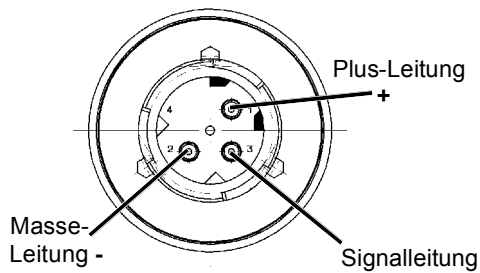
Anschlussbelegung Drucksensor 441 040 (007)/013/015 0 (Ausführung mit DIN-Bajonett)
